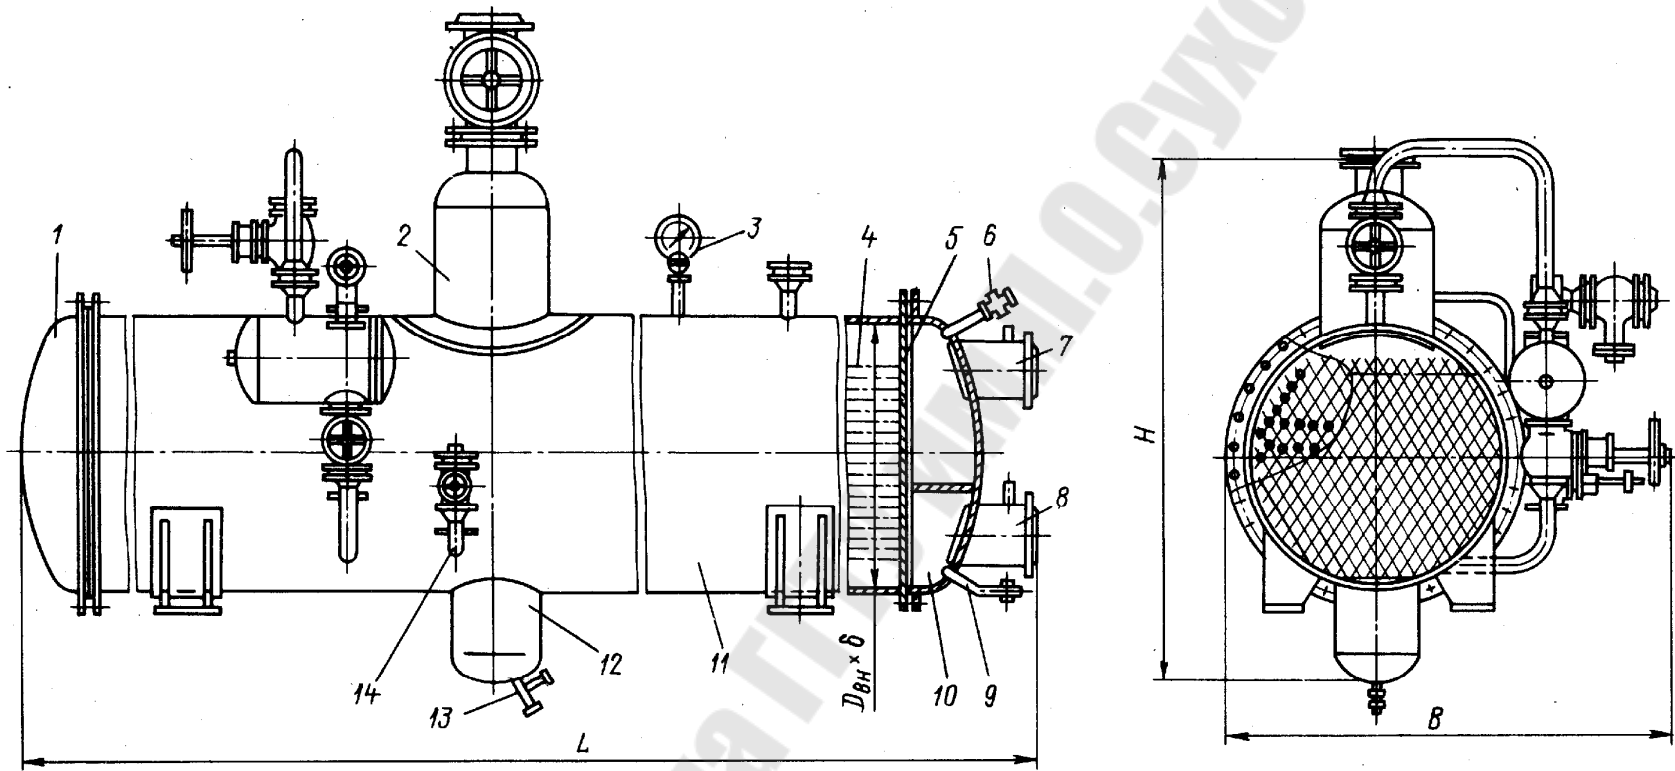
15 [16]. Аммиачный кожухотрубный испаритель затопленного типа: 1, 10 – крышки; 2 – сухопарник; 3 – манометр; 4 – трубы; 5 – трубная решетка; 6 – вентиль для спуска воздуха; 7, 8 – штуцера для входа и выхода рассола; 9 – слив рассола; 11 – корпус; 12 – маслоотстойник; 13 – кран для спуска масла; 14 – патрубок для входа жидкого аммиака
